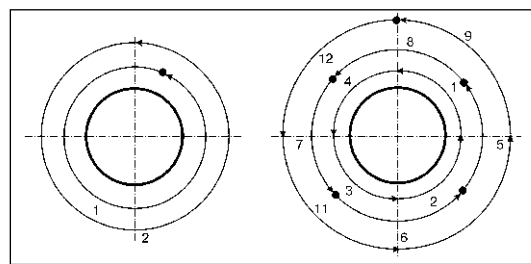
Порядок наложения слоев при сварке горизонтальных стыков труб одним сварщиком
